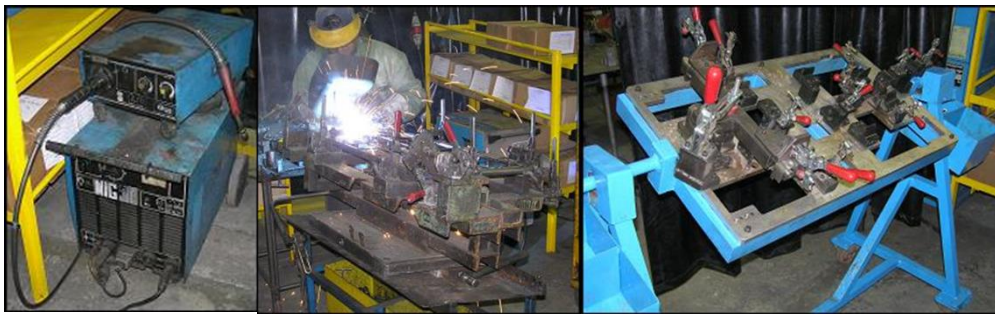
16 - Aparelho de soldadura MIG/MAG e Suportes para o Produto.
